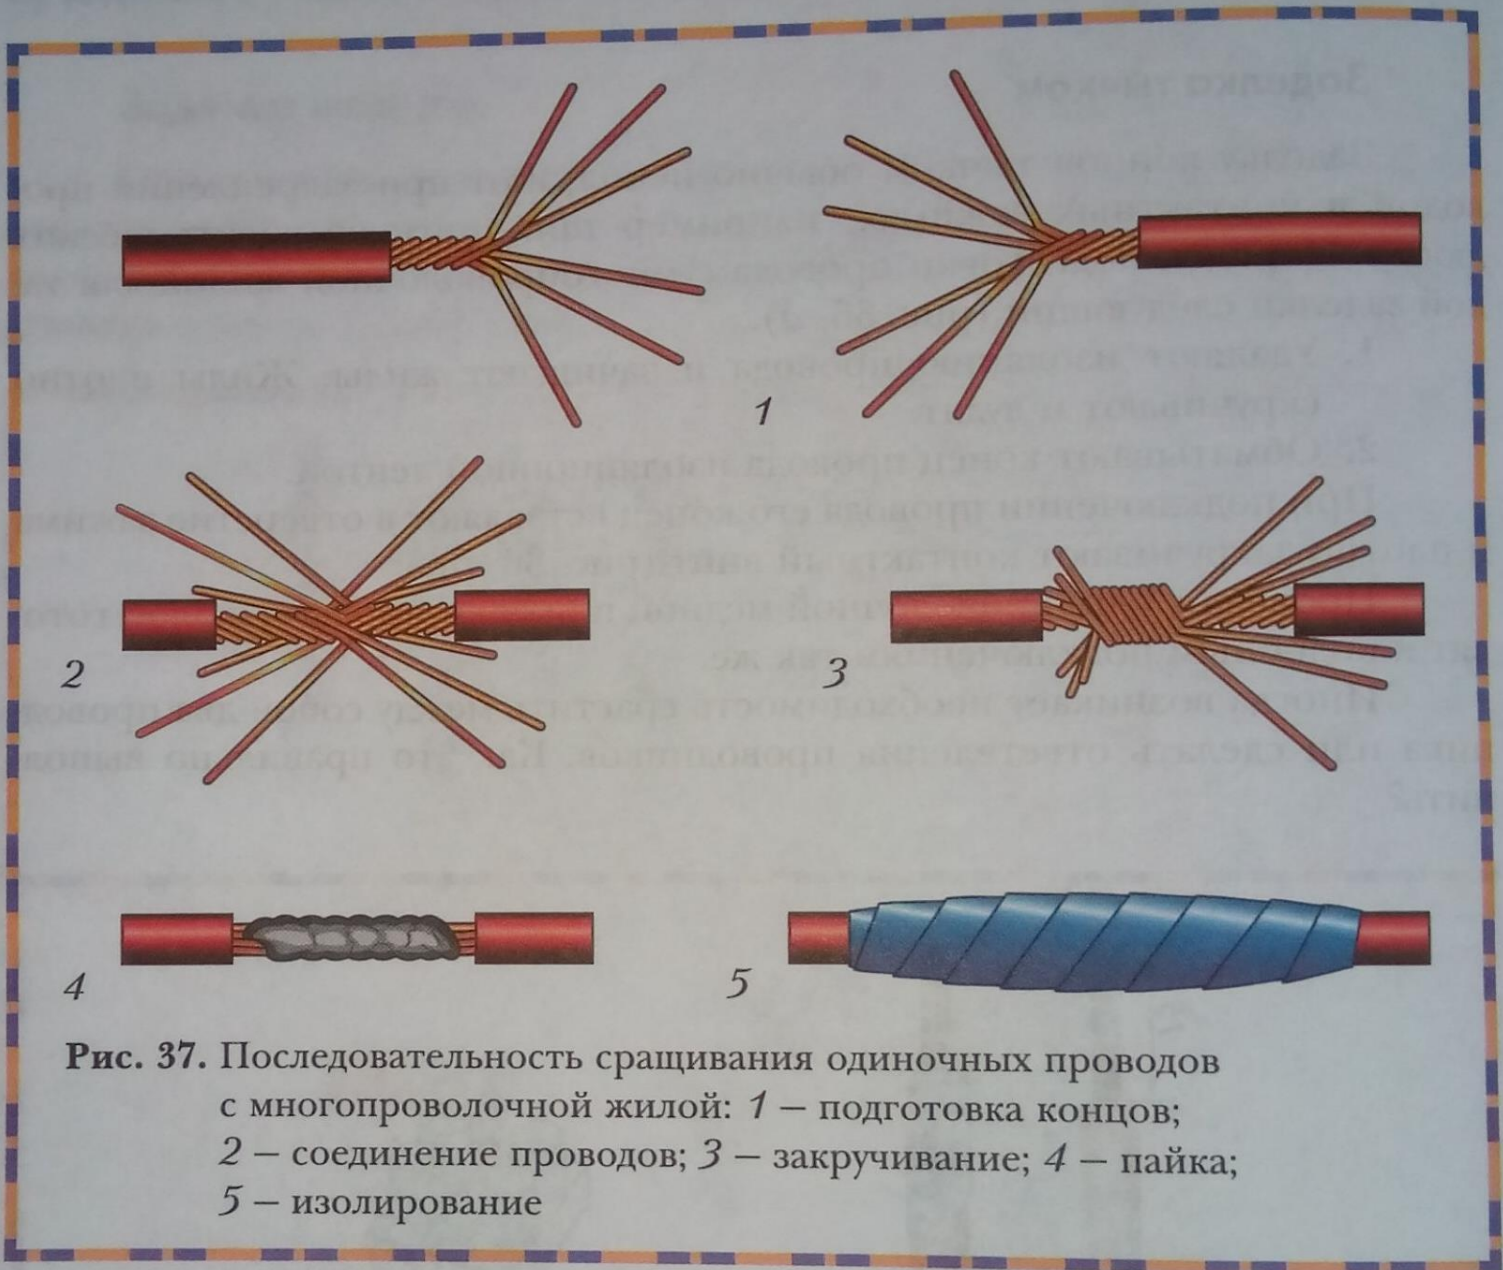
Последовательность сращивания одиночных проводов с многопроволочной жилой: 1 – подготовка концов; 2 – соединение проводов; 3 – закручивание; 4 – пайка; 5 – изолирование
